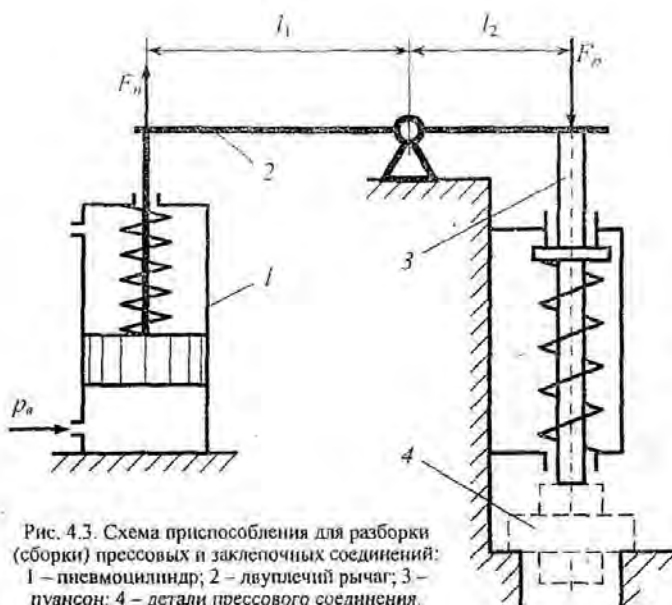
Схема приспособления для разборки (сборки) прессовых и заклепочных соединений: 1 – пневмоцилиндр; 2 – двуплечий рычаг; 3 – пуансон; 4 – детали прессового соединения.
